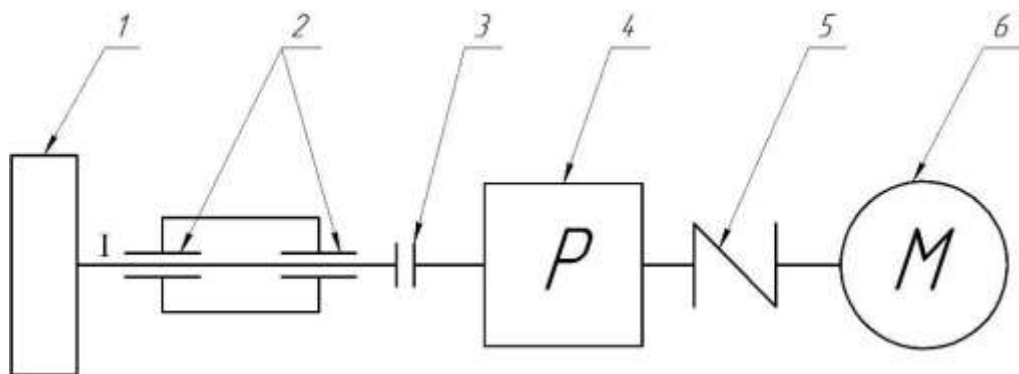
Кінематична схема колісного вузла: 1 – механум-колесо, 2 - підшипникова пара (ПП), 3 – жорстка муфта, 4 – редуктор, 5 – гнучка муфта, 6 – двигун постійного струму.
